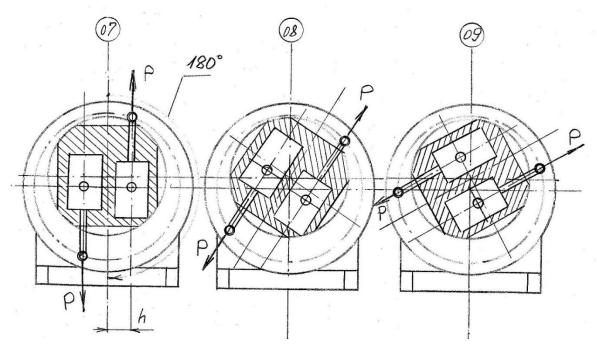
Чертёж позиций поршней и цилиндров роторного двигателя в процессе вращения
